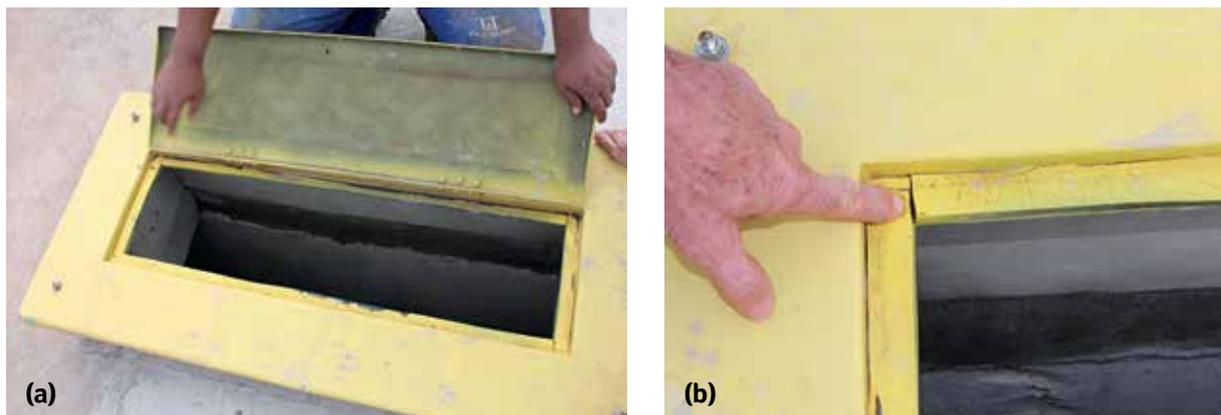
a) Tampa de PRFV para inspeção de separador trifásico; b) Detalhe de falha no elemento de vedação da tampa de inspeção.
